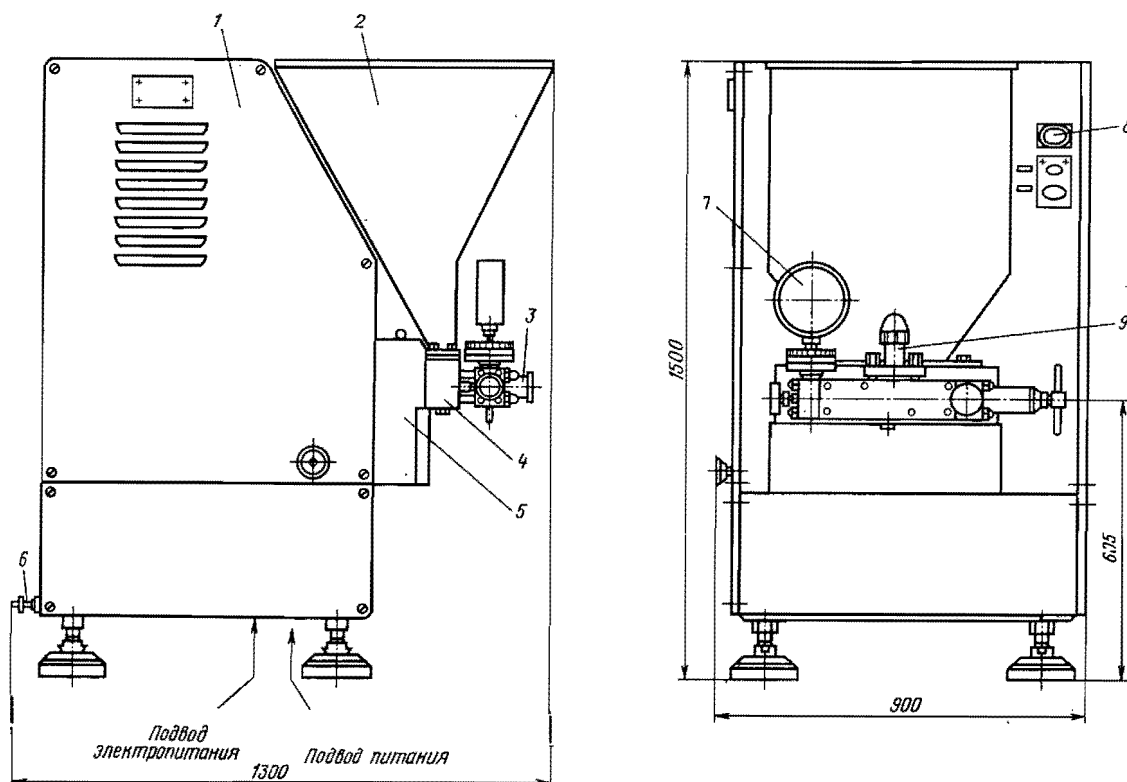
Габаритный чертеж гомогенизатора марки А1-ОГ2-С:
